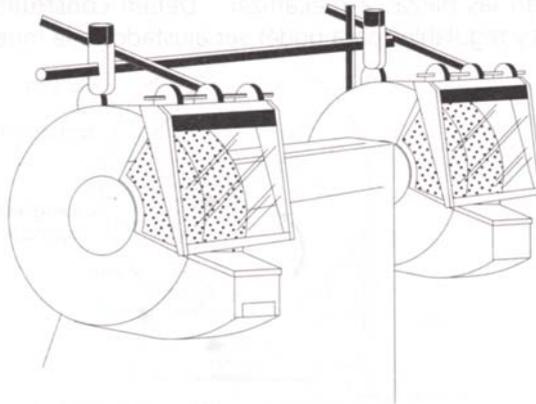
Pantalla montada sobre soporte adaptable a cualquier esmeriladora
